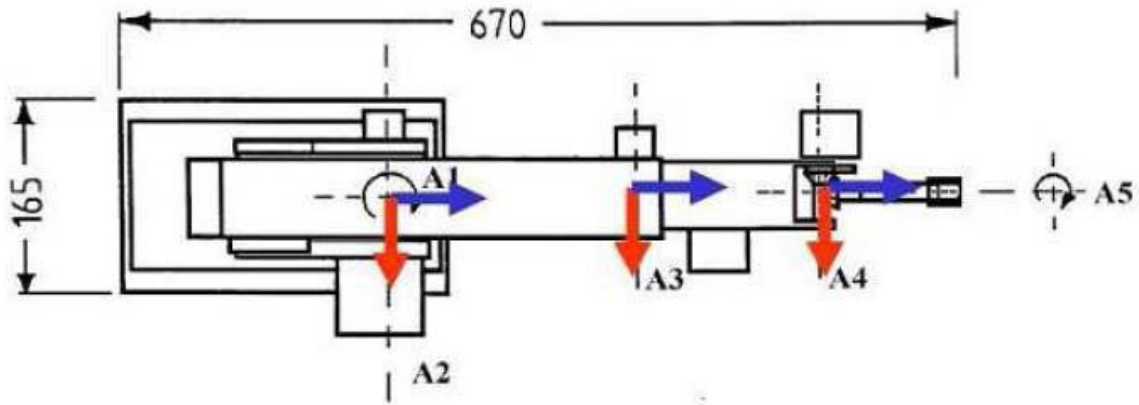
Les dimensions du robot ROB3 (vue de haut).
